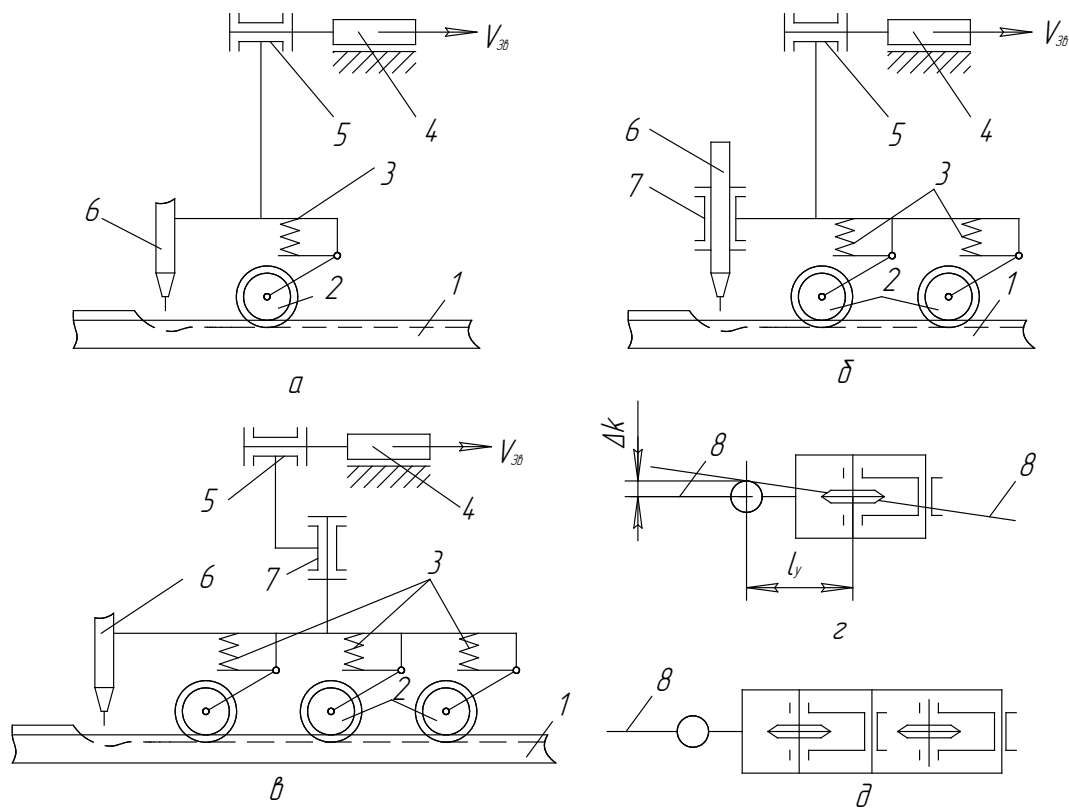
Схеми пристроїв прямої дії для направлення зварювального інструмента по лінії з'єднання:
